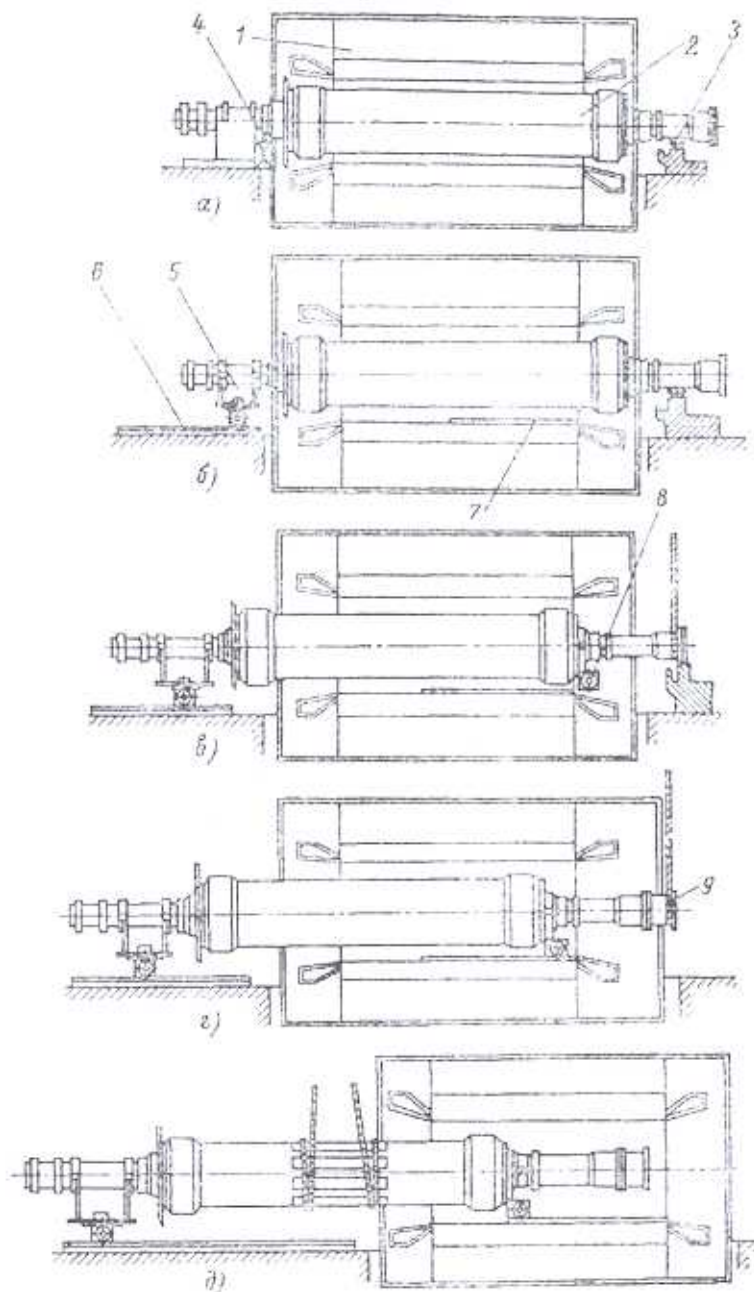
Вывод ротора двумя тележками для турбогенераторов с вынесенными подшипниками [1]:
